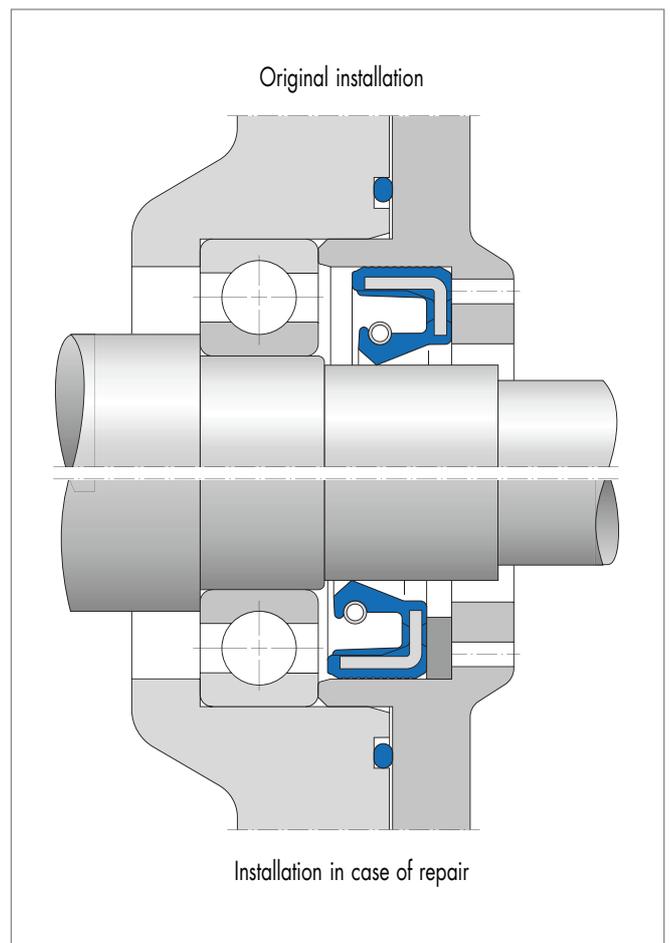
Montage bei Reparatur und Montage des Aggregats / Agregatın montajı ve onarımı sırasında montaj / Montaż w przypadku naprawy i montażu urządzenia / Монтаж при ремонте и сборке агрегата
